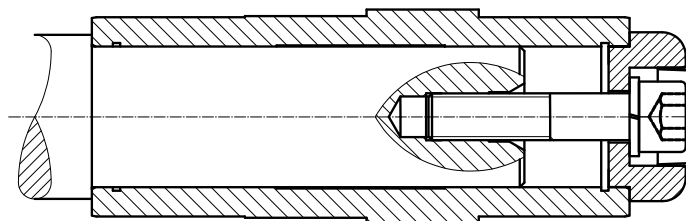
Getriebe auf Welle mit Anlageschulter mit Befestigungselement befestigt
